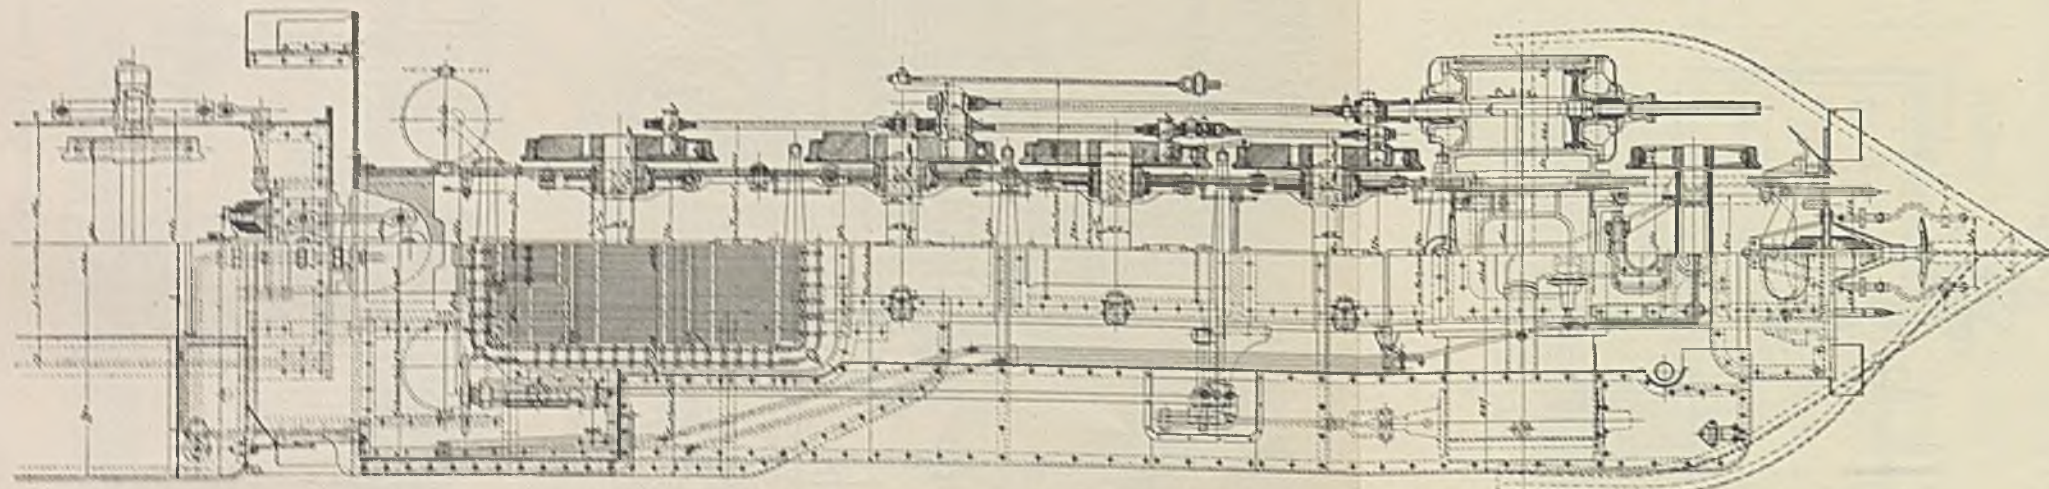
1/2-Wagrechtsschnitt, 1/2-Grundriss.
